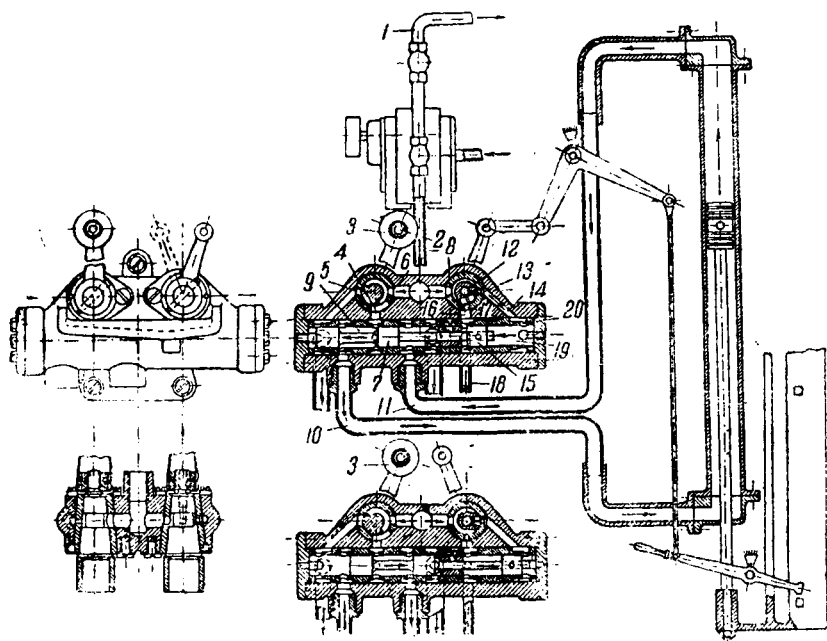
Схема гидравлического привода для возвратно-поступательного движения стола станка „Дискус“
